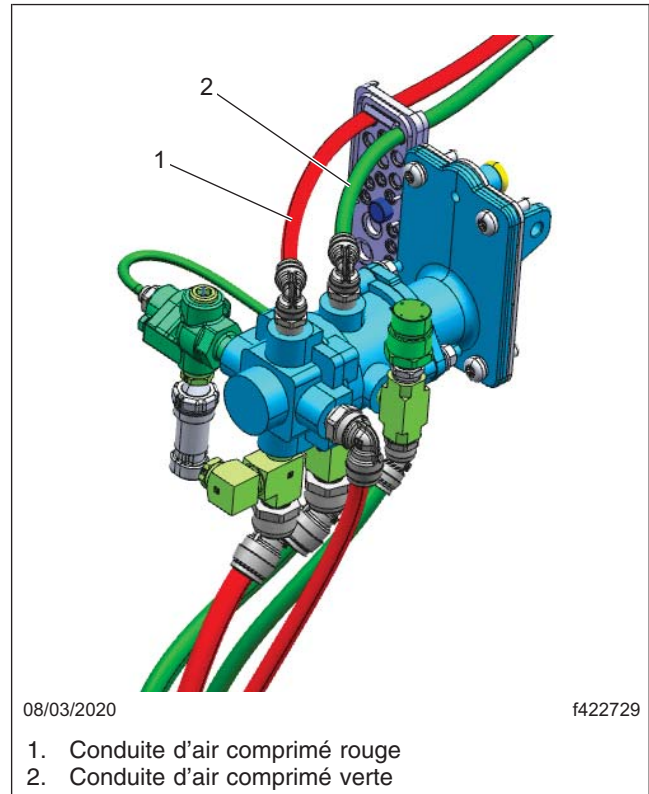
, Débranchement des conduites d'air comprimé rouge et verte
